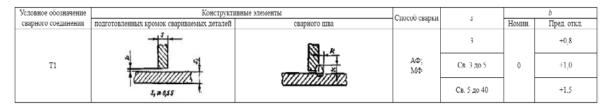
Эскиз сварного соединения (Т1)
